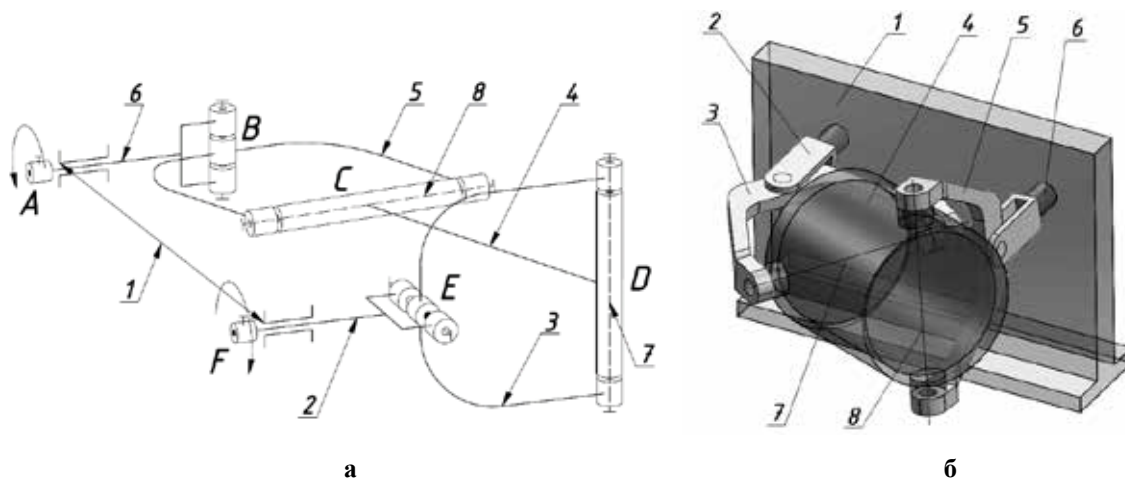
а – кинематическая схема «базовой» конструкции механизма, б – модель машины
